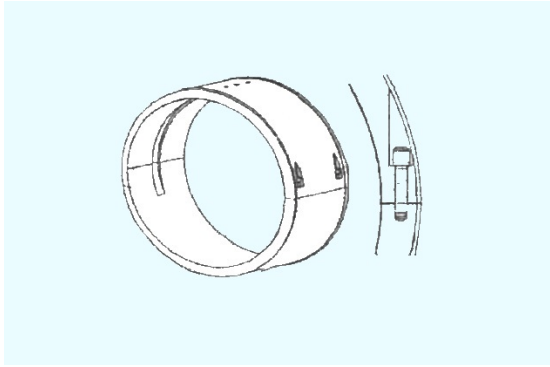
Вкладыши рамовых подшипников дизелей типа МС-С
